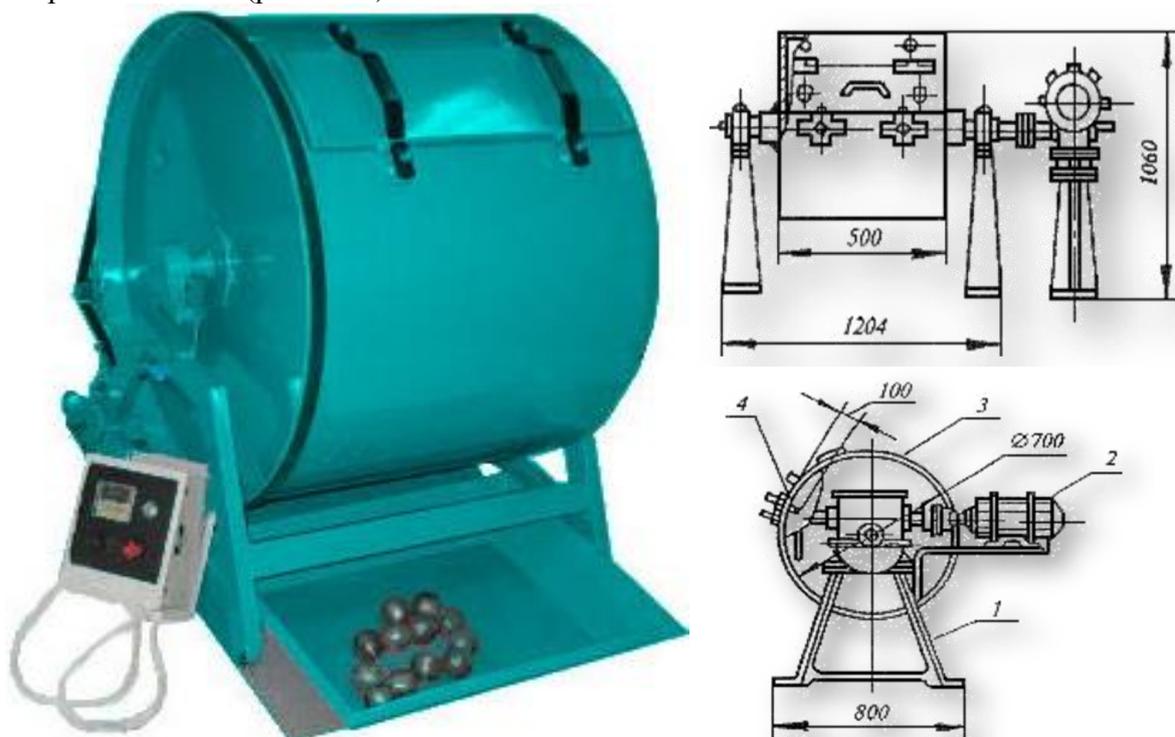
Полочный барабан: 1 – станина; 2 – двигатель; 3 – барабан; 4 – полка барабана
